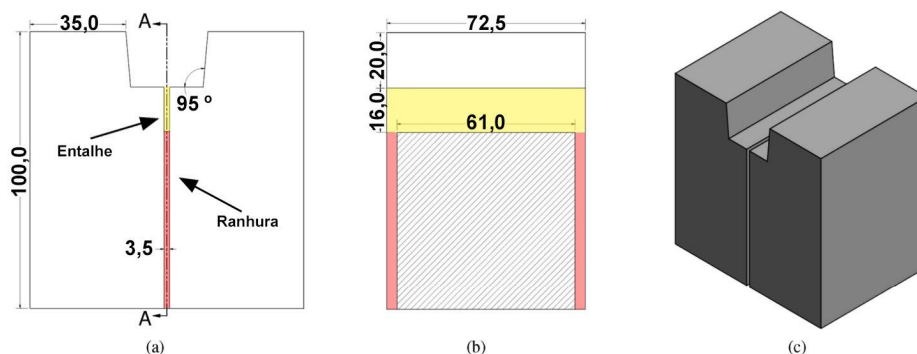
Geometria do corpo de prova e dimensões (em mm). (a) Vista frontal, (b) corte A-A da seção transversal e (c) perspectiva isométrica. Adaptada⁽⁹⁾.
